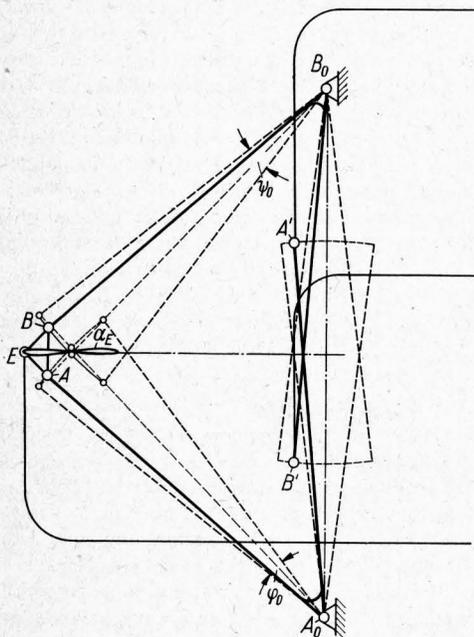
Doppelschwinge mit umlaufendem Koppelantrieb zur Erzeugung einer Dreifach-Schwingbewegung.
